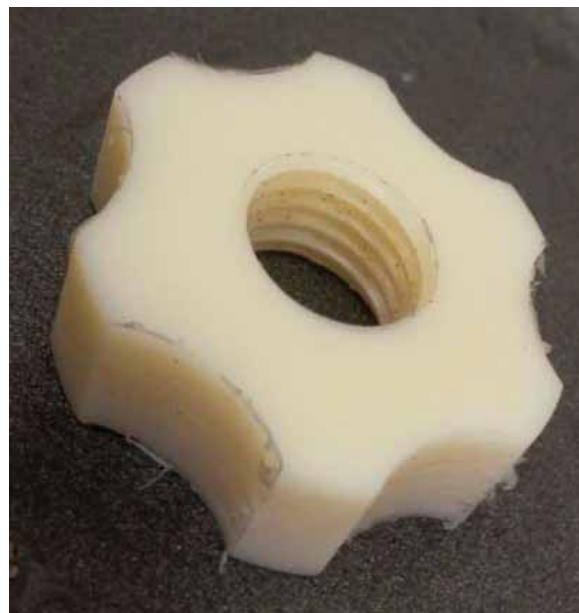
Внешний вид детали «звёздочка», изготовленной на токарном станке с использованием универсального узла
